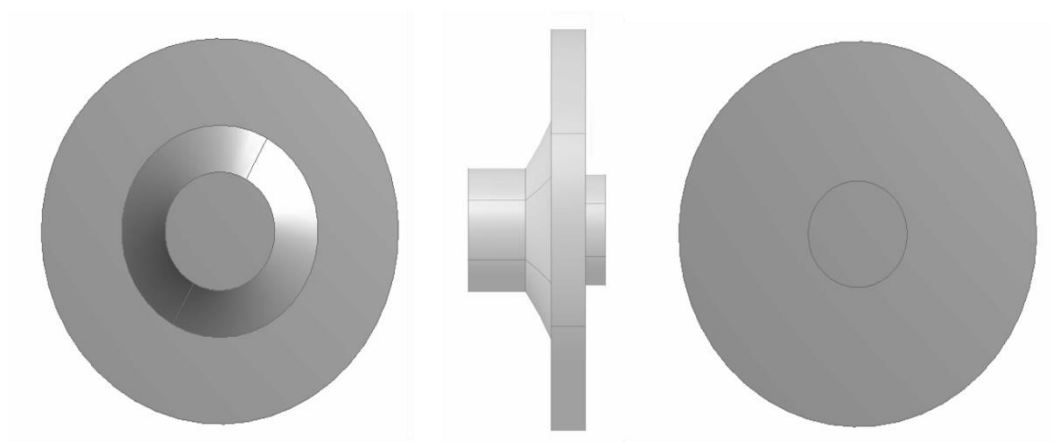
Molde para rotor SCX1. Vista superior, lateral e inferior (autor)
